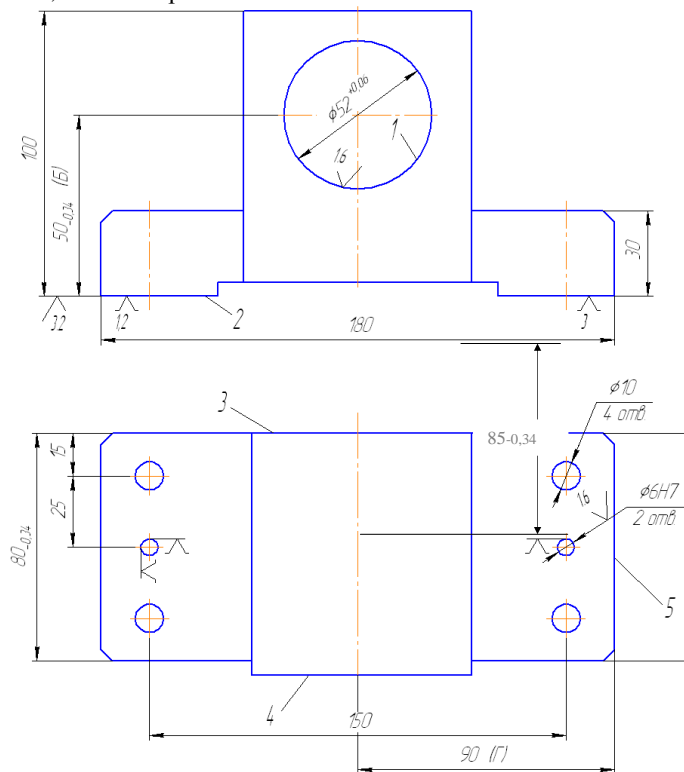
Корпус підшипника; креслення та схема установлення при обробленні отвору  $\varnothing 52^{+0,06}$  мм.
